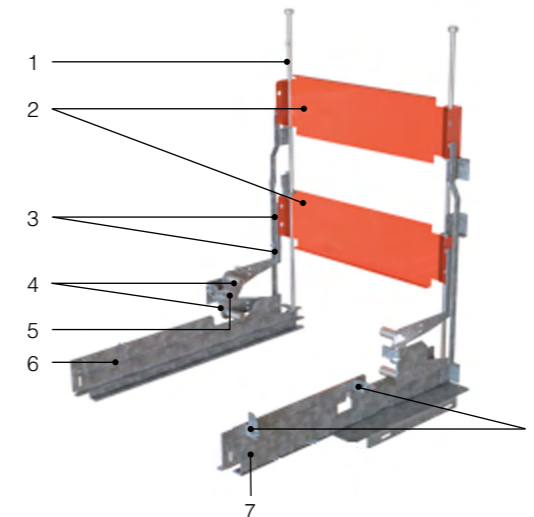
Шторочный механизм с направляющими полозьями
